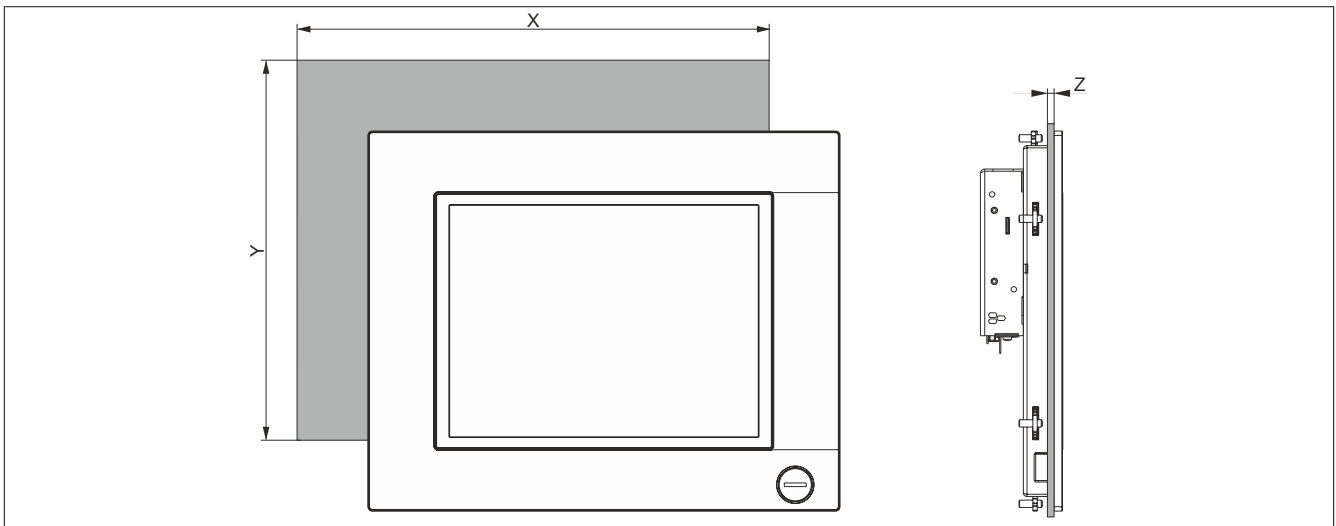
Устройство Panel PC 2200 на базе панелей AP1000 с удерживающими зажимами — монтажный чертеж
